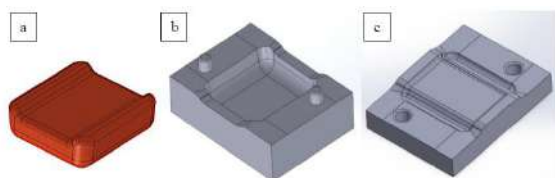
Prototipo de cojín (a), base molde cojín (b), tapa molde cojín (c).
